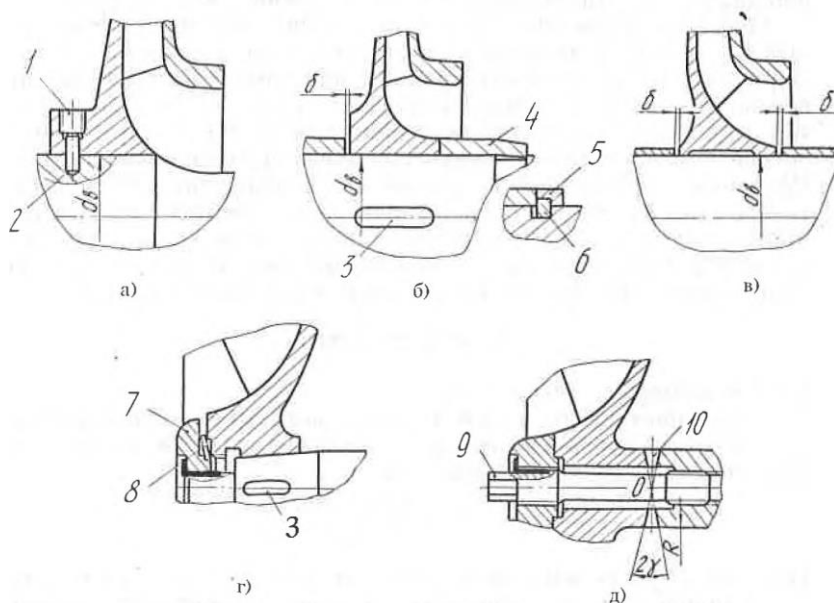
Узел крепления рабочего колеса: 1 - винт; 2 -штиф т; 3 - шпонка; 4 -фиксирующая втулка; 5 -замковое кольцо; 6 - полукольца; 7 - гайка; 8 - пружинная шайба; 9 - стяжная шпилька; 10 - торцовое шлицевое соединение;  $d_B$  - диаметр вала
